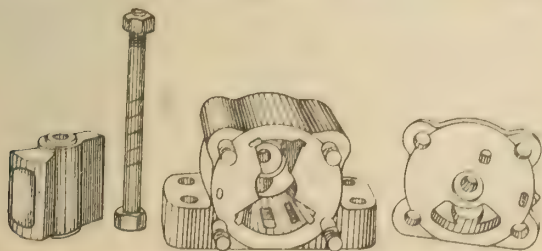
Steuermechanismus der Bohrmaschinen der Pratt Machinery Co., St. Louis.
